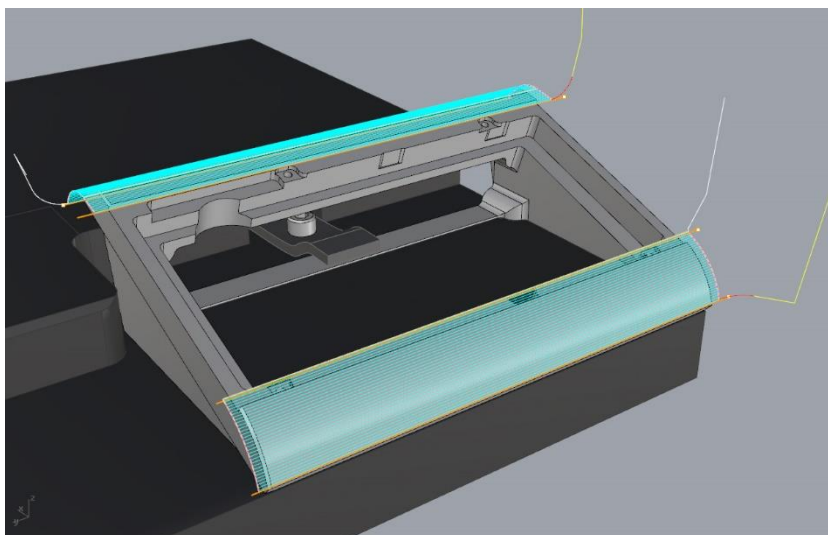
První upnutí – dokončování fréza 4 mm – Standard Drill
